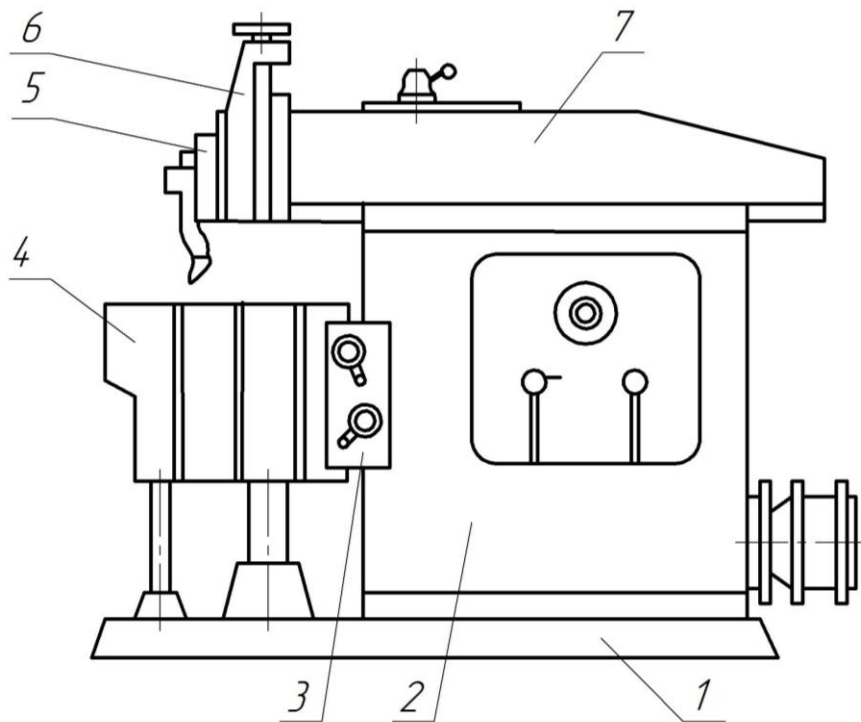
Загальний вигляд поперечно-стругального верстата
